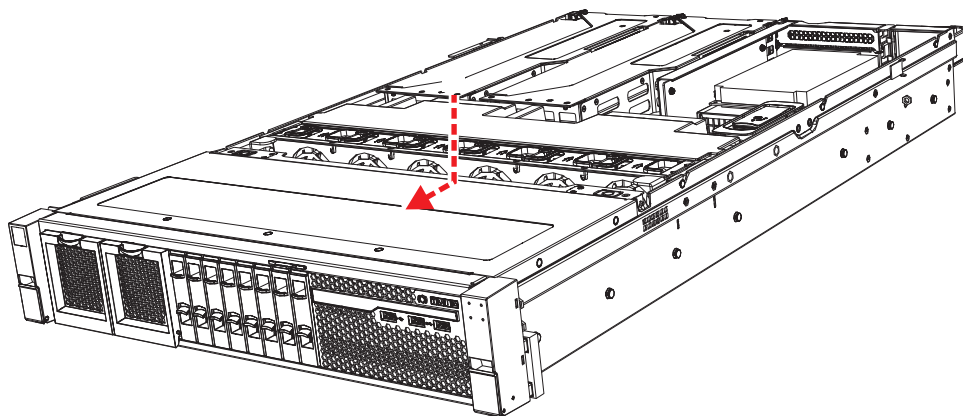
Substituindo a tampa frontal superior do 2145-SV1
